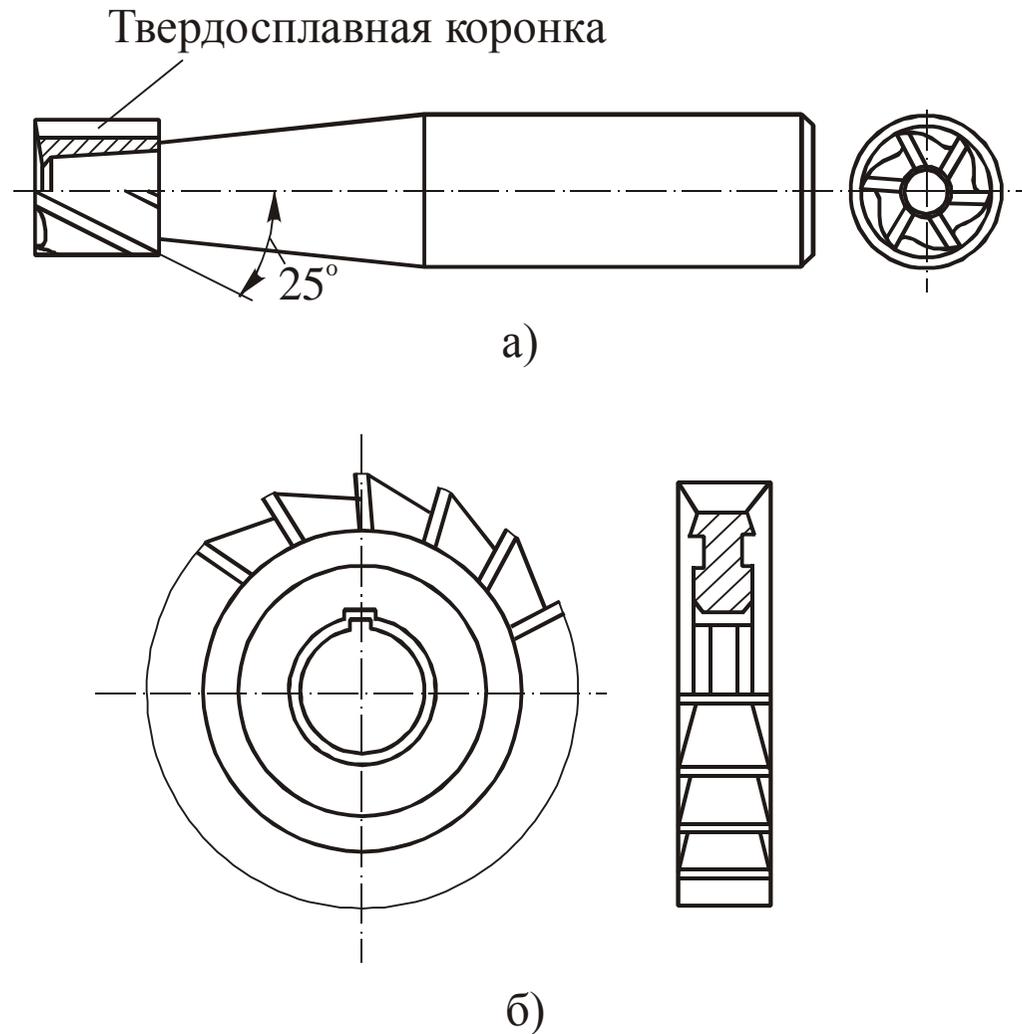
Мелкогабаритные твердосплавные фрезы: *а* – концевая фреза с монолитной твердосплавной режущей частью; *б* – дисковая твердосплавная фреза
